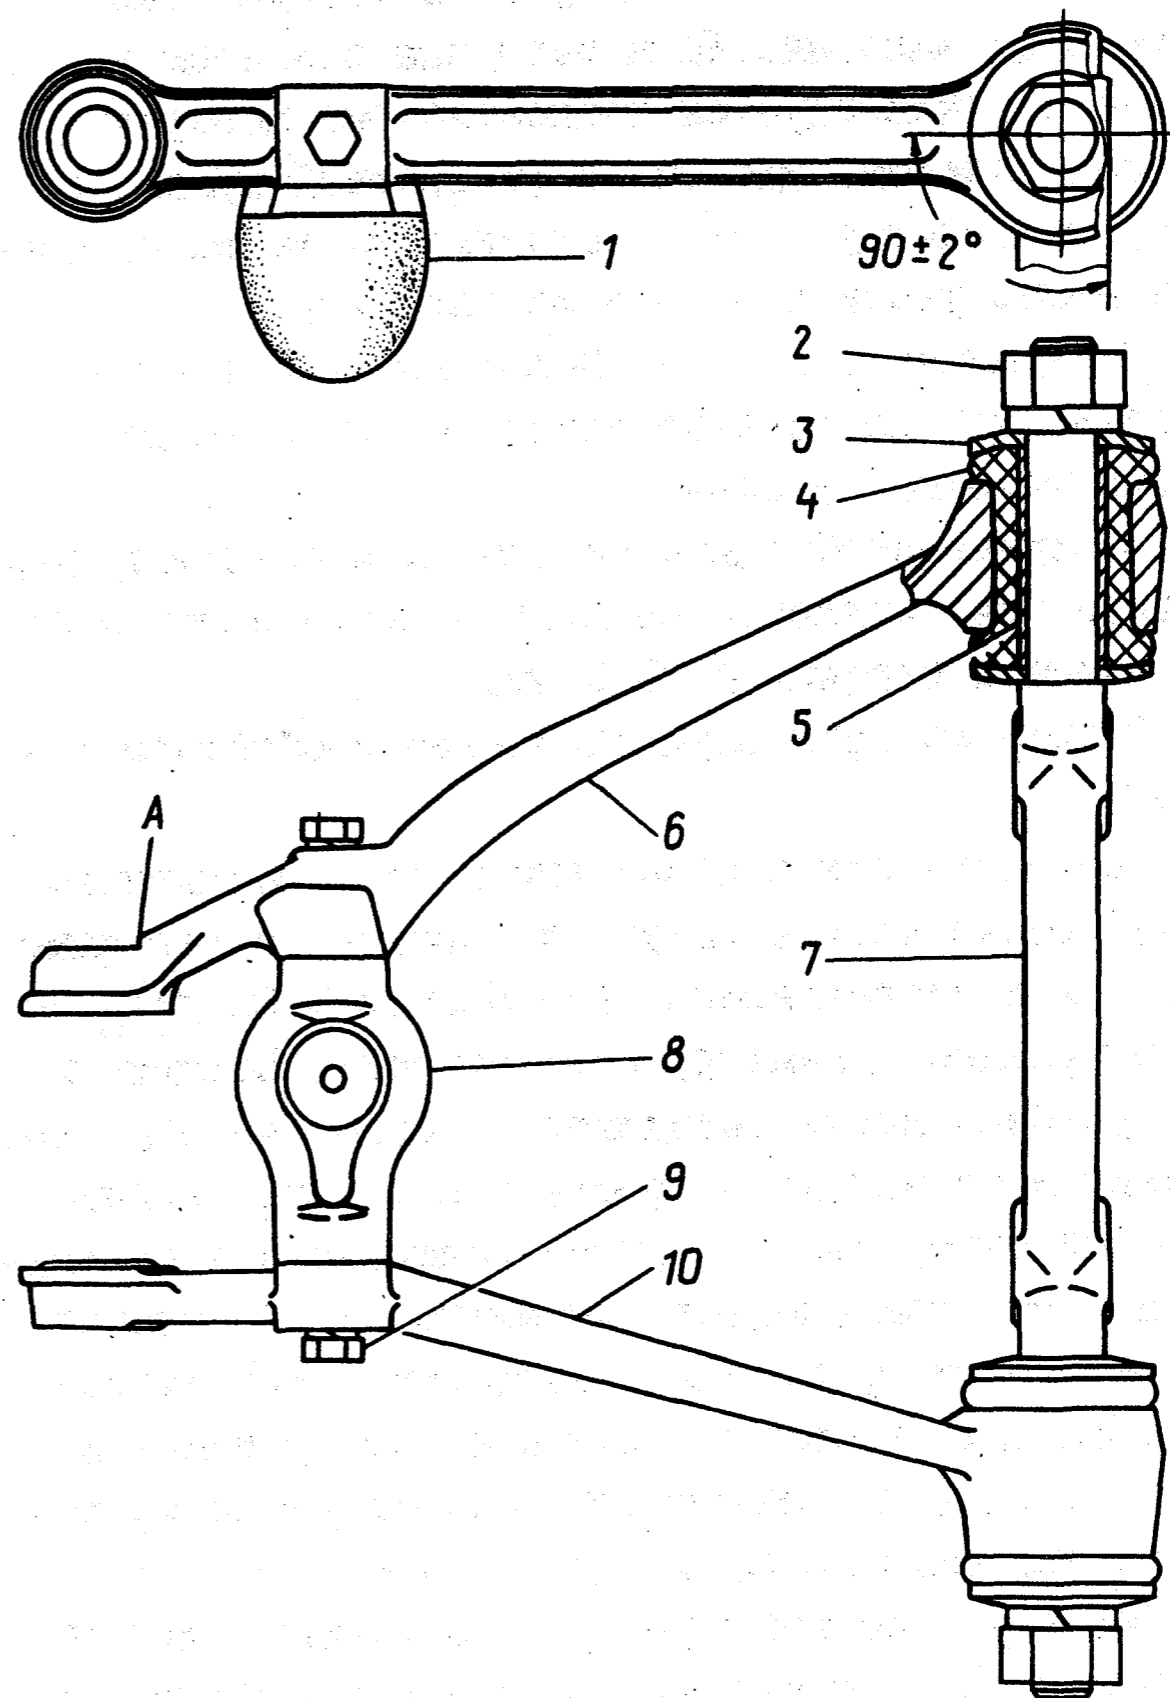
Верхние рычаги подвески: А - выступ; 1 - буфер хода отдачи; 2 - гайка; 3 - шайба сферическая; 4 - втулка резиновая; 5 - втулка распорная; 6 - рычаг передний; 7 - ось; 8 - опора буфера; 9 - болт; 10 - рычаг задний
